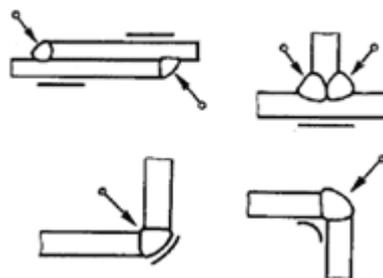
Схемы просвечивания сварных соединений
